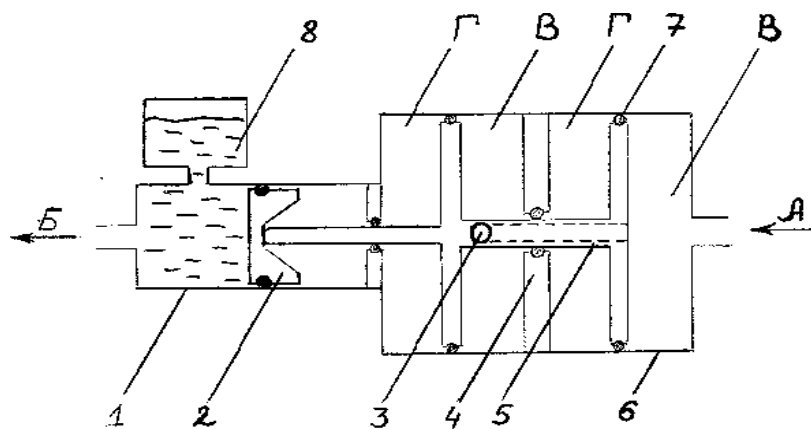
Схема пневматичного підсилювача з головним гідравлічним гальмівним циліндром: 1 – головний гідравлічний гальмівний циліндр; 2 – поршень; 3 – радіальний отвір; 4 – проставка; 5 – шток із поршнями; 6 – корпус пневматичних циліндрів; 7 – ущільнення; 8 – бачок для гальмівної рідини; А - підведення стисненого повітря від гальмівного крана; Б - виведення в гідравлічну гальмівну систему; В – силові порожнини; Г – атмосферні порожнини
